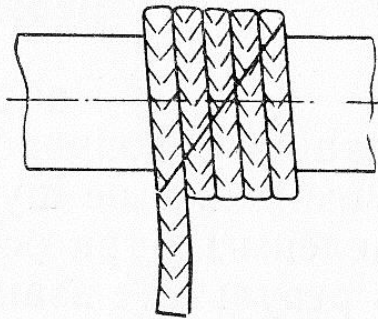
Виготовлення кілець для сальникової набивки
